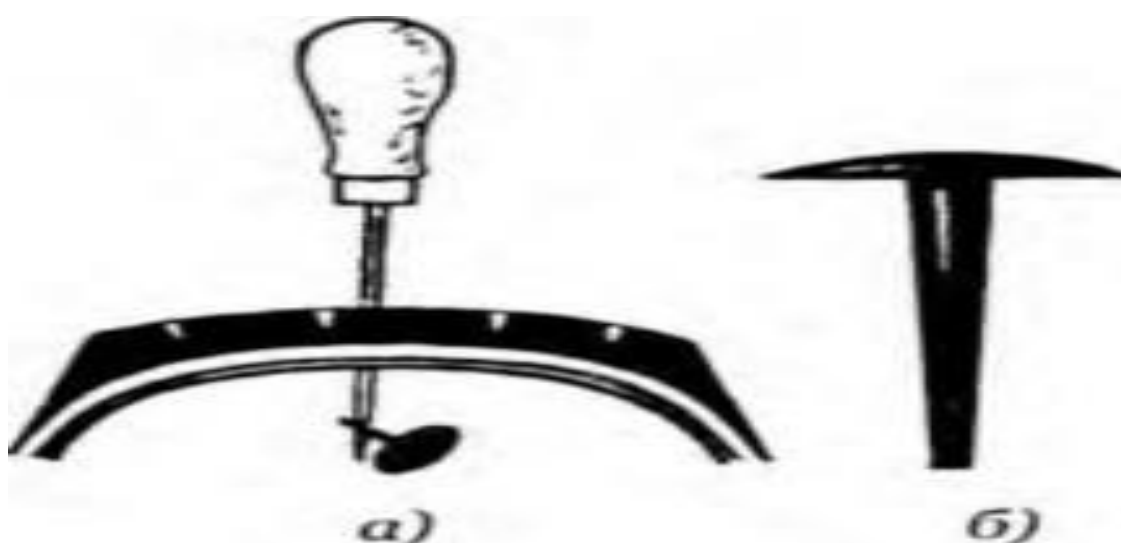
Ремонт проколотых шин: а — установка грибка в отверстиепрокола; б — грибок
